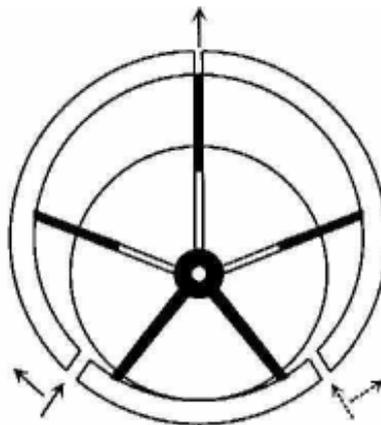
Representação do Motor Pneumático de Palhetas.
